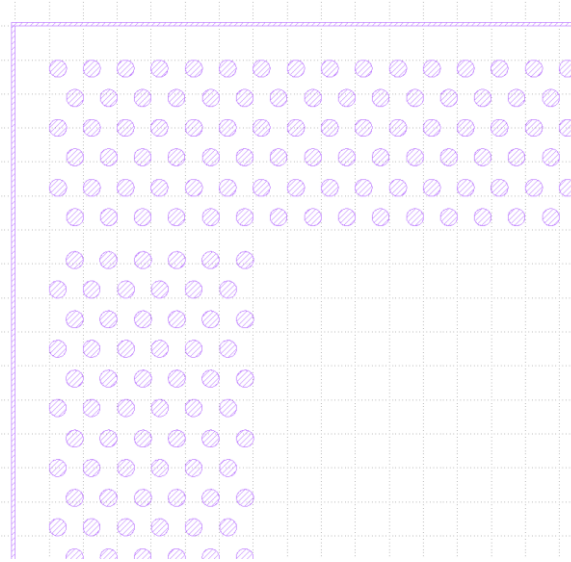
Layout Assembly-Rahmen; für LASER-Lochung (Detailansicht)
